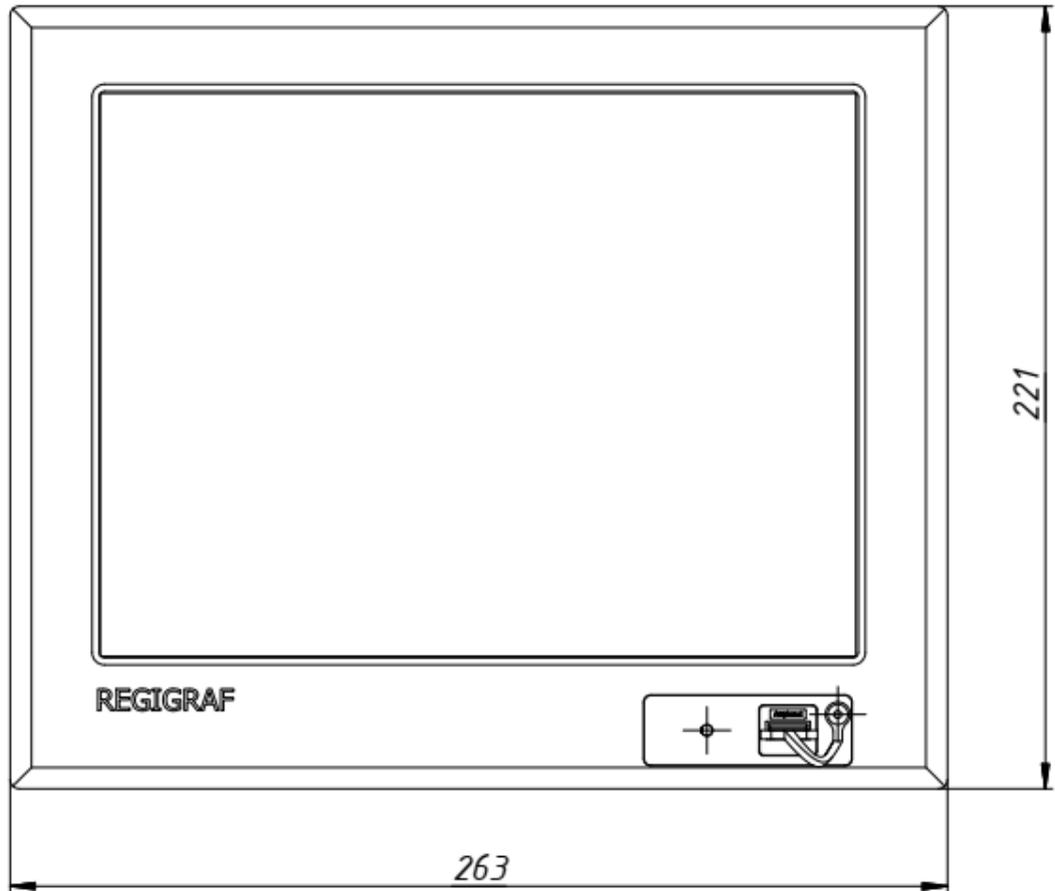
Габаритный чертёж прибора в исполнении Ф1772–1, вид спереди
